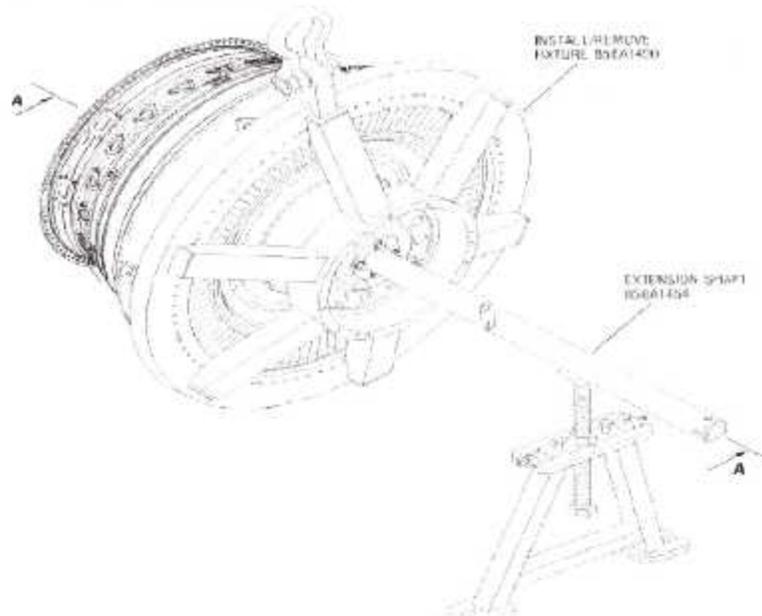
Installation du Dispositif Installation/Enlèvement, 856A490G04 sur l'ensemble du carter HPT et 1 étage stator de LPT.
